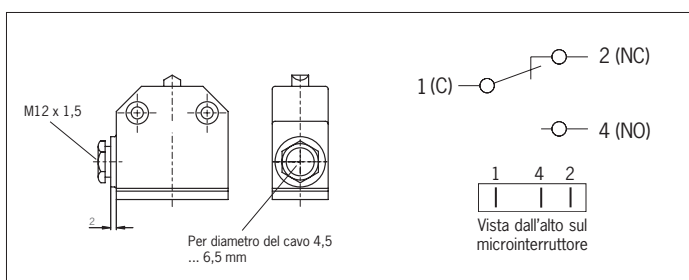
Dimensioni/schema di collegamento N01.550MC2018 con collegamento a pressacavo
